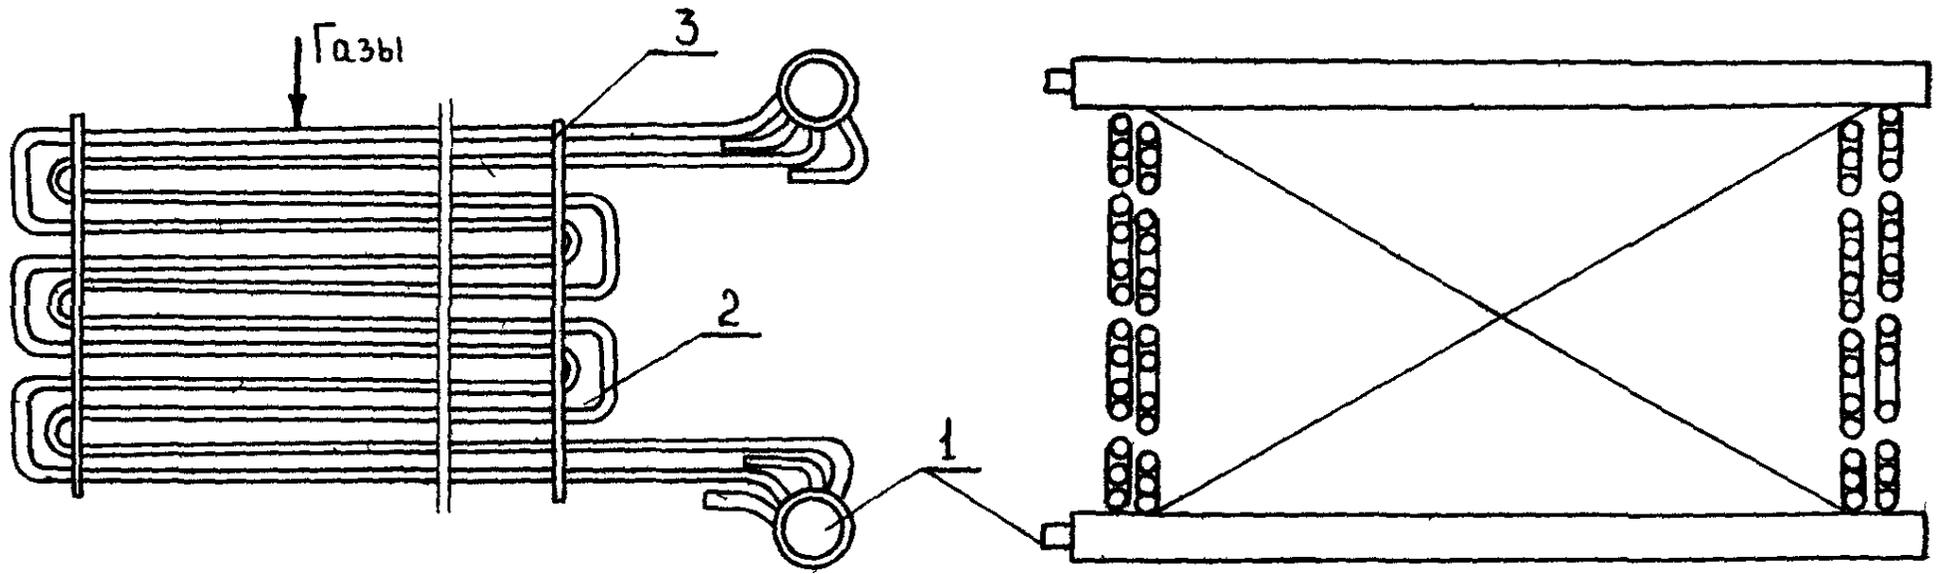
Блок регулировочной поверхности вторичного пароперегревателя (правый)
